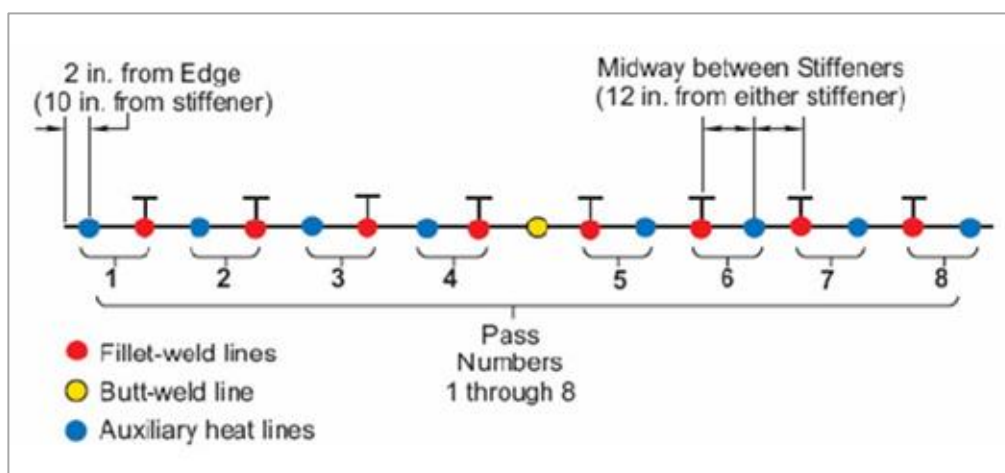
Sequências de linhas de calor e soldaduras [35]
